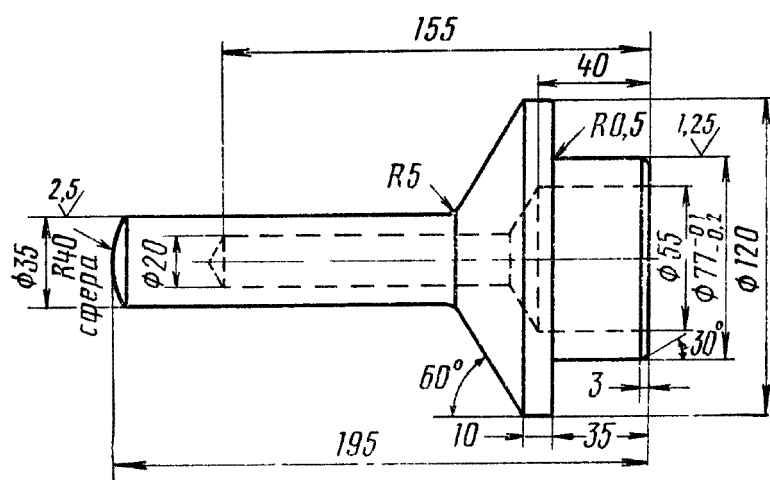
Оправка для запрессовки подшипников промежуточного вала
